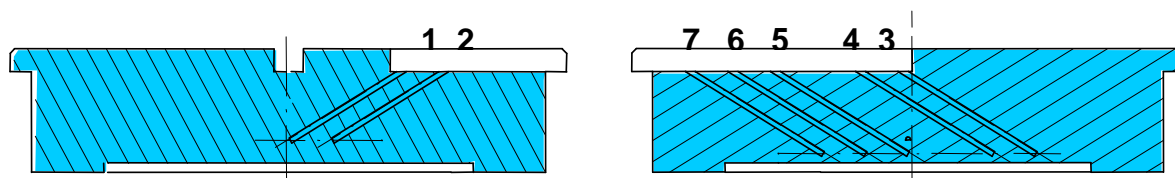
Positions des thermocouples dans le tas plan instrumenté.
